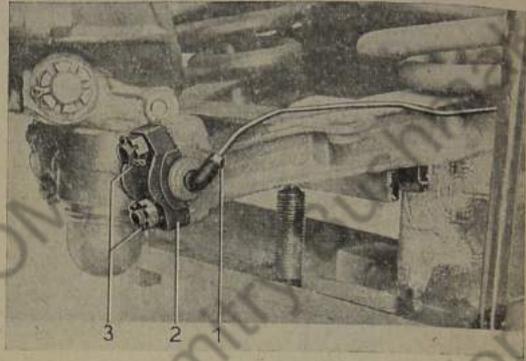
Querlenkerdeckel für Lagerzapfen abschrauben
